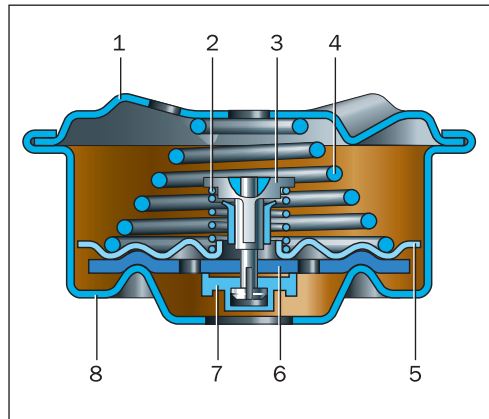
Устройство пробки радиатора системы охлаждения: 1 — крышка; 2 — пружина впускного клапана; 3 — стержень впускного клапана; 4 — пружина выпускного клапана; 5 — тарелка пружины выпускного клапана; 6 — выпускной клапан; 7 — впускной клапан; 8 — корпус пробки
